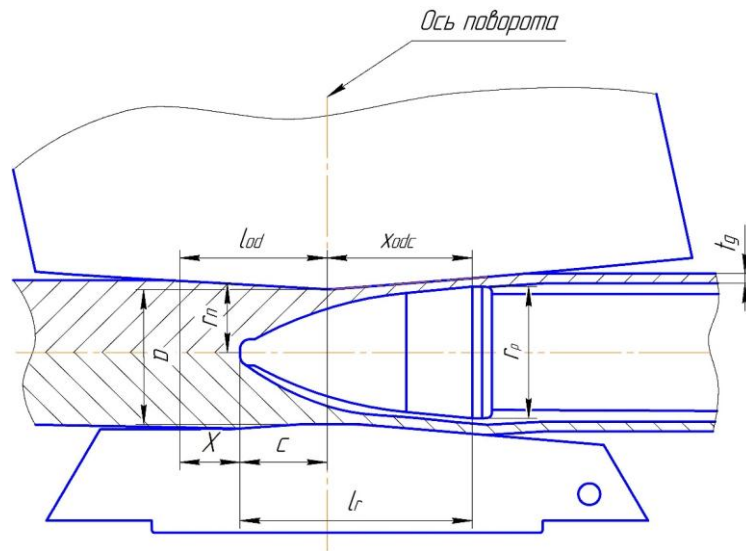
Схема очага деформации при двухвалковой винтовой прошивке
